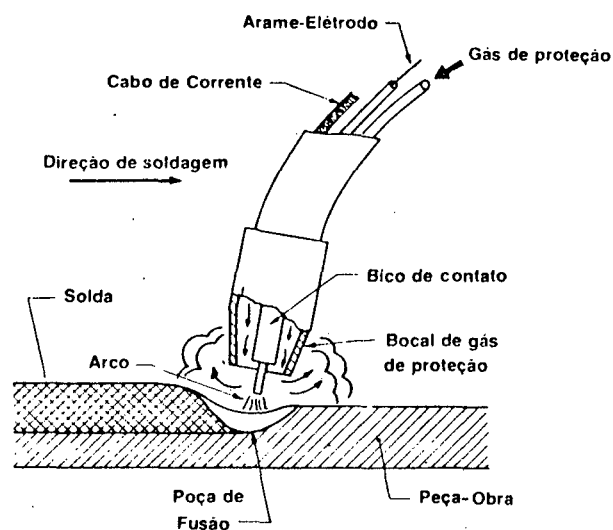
Representação esquemática do extremo de uma pistola de soldagem MIG/MAG [1].
